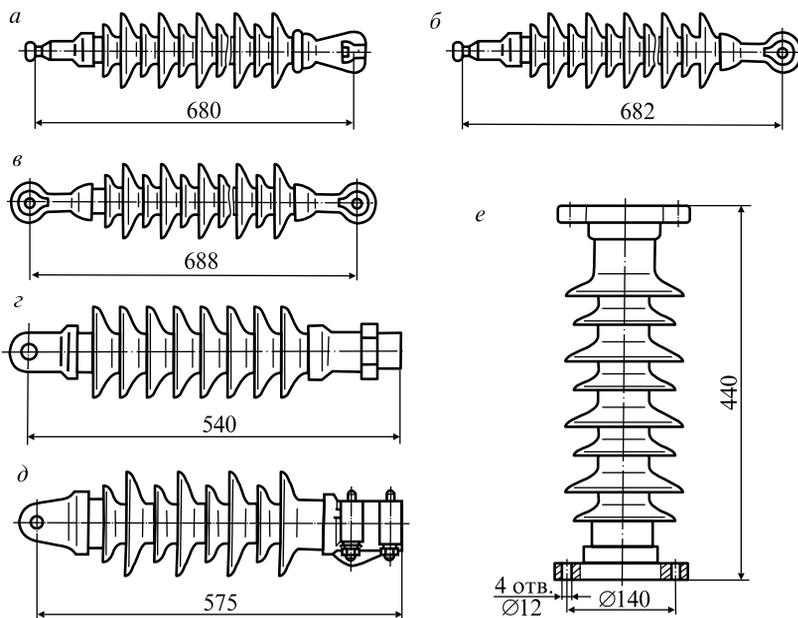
Полимерные изоляторы с ребристым защитным чехлом из кремнийорганической резины: а, б — подвесные ПСКр120/1,5; в — натяжной НСКр 120/1,5; г — фиксаторный ФСКр70/0,9; д — консольный КСКр70/0,9; е — опорный ОСКр70/0,9
